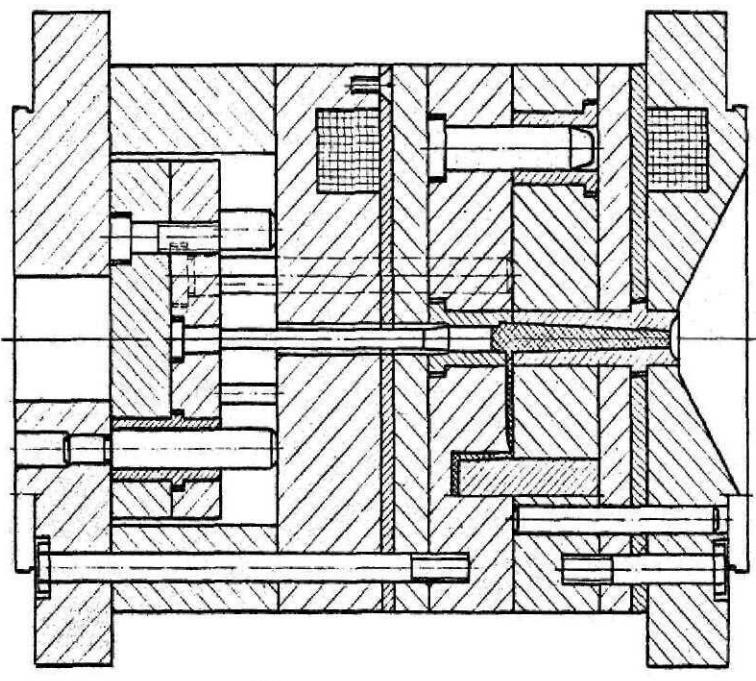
Пресс-форма литьевая для переработки реактопластов методом литья под давлением
